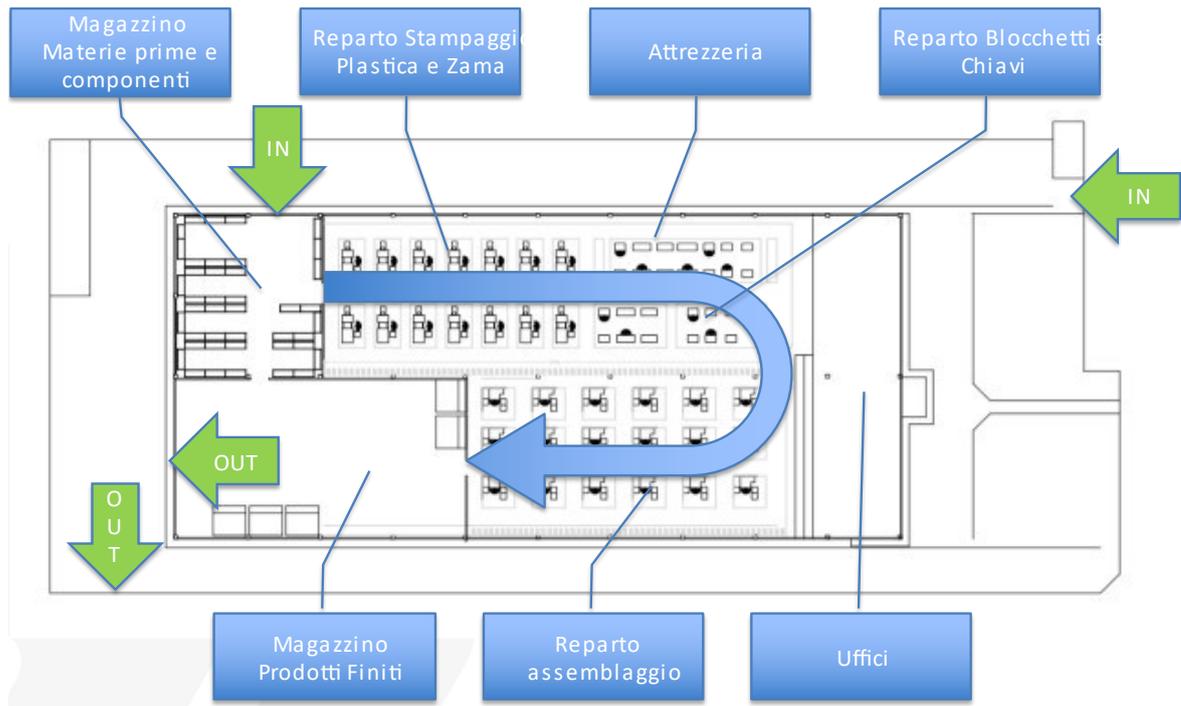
Prima bozza nuovo layout Plant di Orbassano - scenario LEAVE
